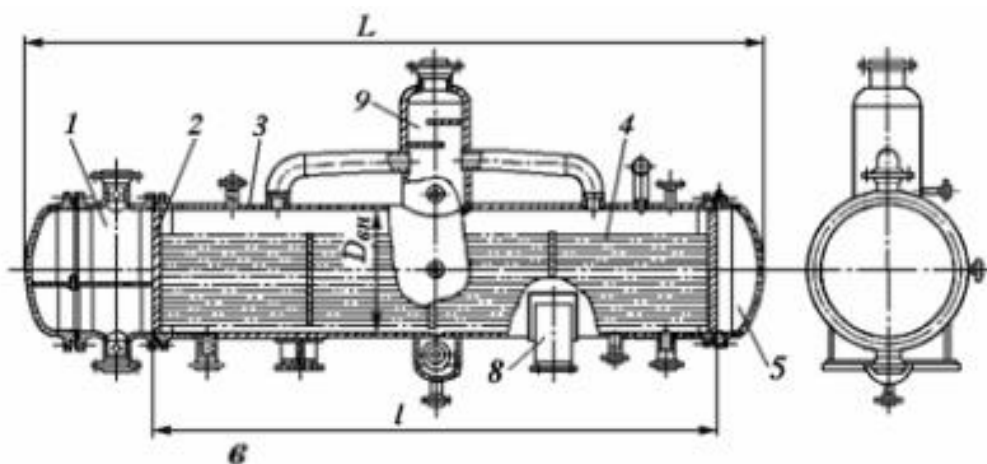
Теплообмінник кожухотрубний з сухопарником - 1 - розподільна камера; 2 - трубна решітка; 3 - корпус; 4 - трубчатка; 5 - кришка еліптична; 6 - переливна планка; 7 - днище; 8 - опора; 9 - сухопарник.
